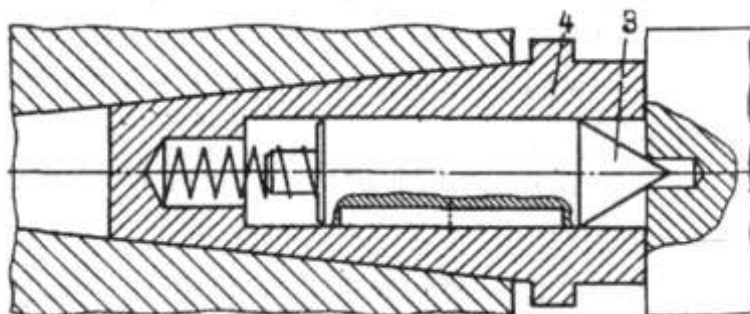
Задний вращающийся центр для обработки заготовок полых деталей
